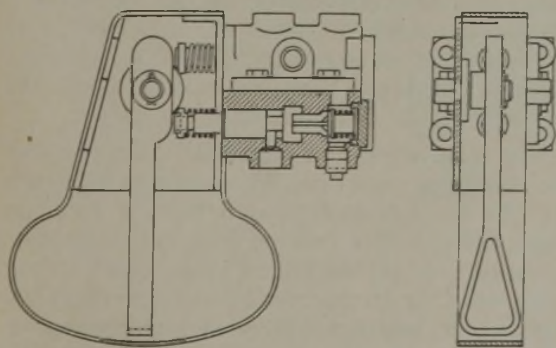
Unfallsicheres Steuer Ventil für Aufschiebevorrichtungen.
